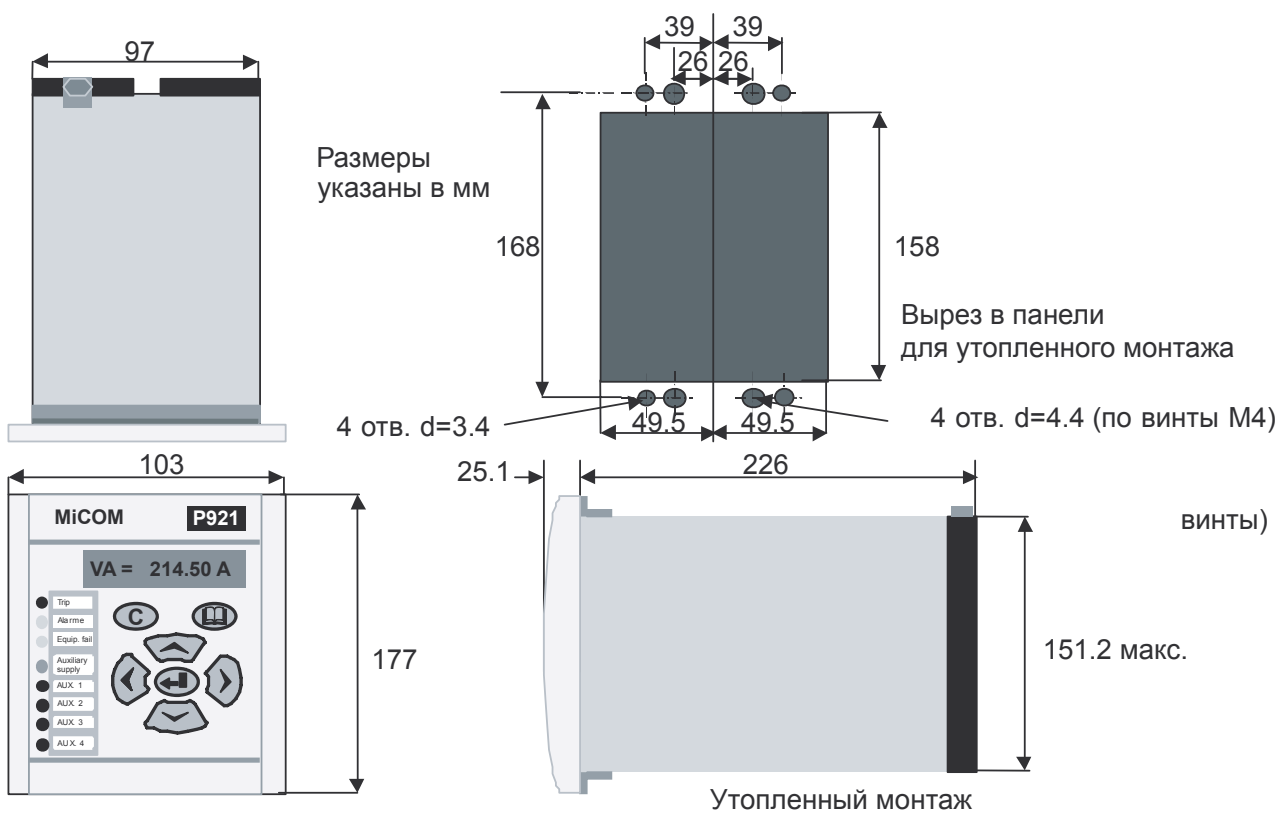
Габаритные размеры корпуса реле MiCOM P921-P922
